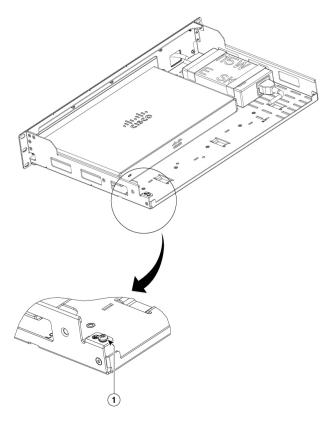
Option de mise à la terre sur la face avant du plateau
